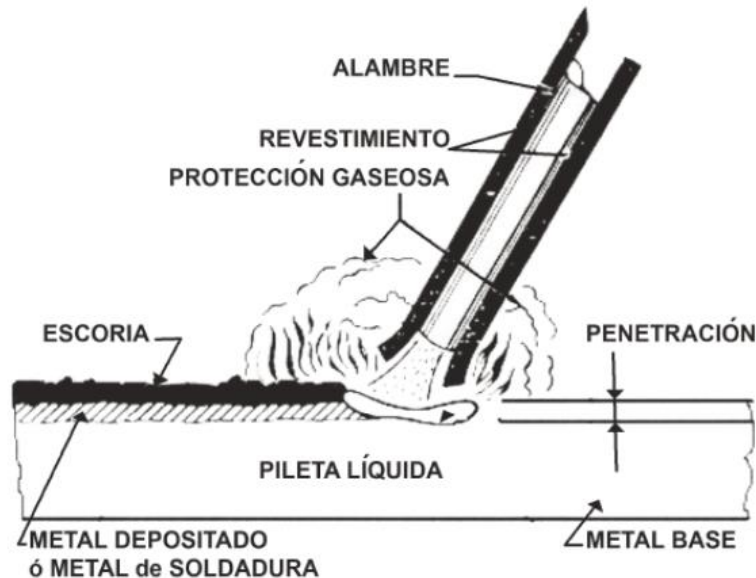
Proceso de soldadura SMAW [26]
